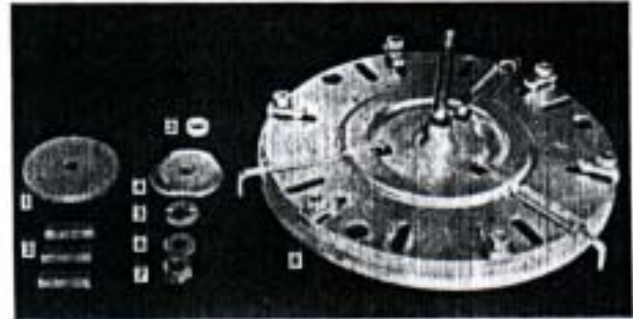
Plato HS-64 para desarmar y ajustar el embrague "AUBURN".
